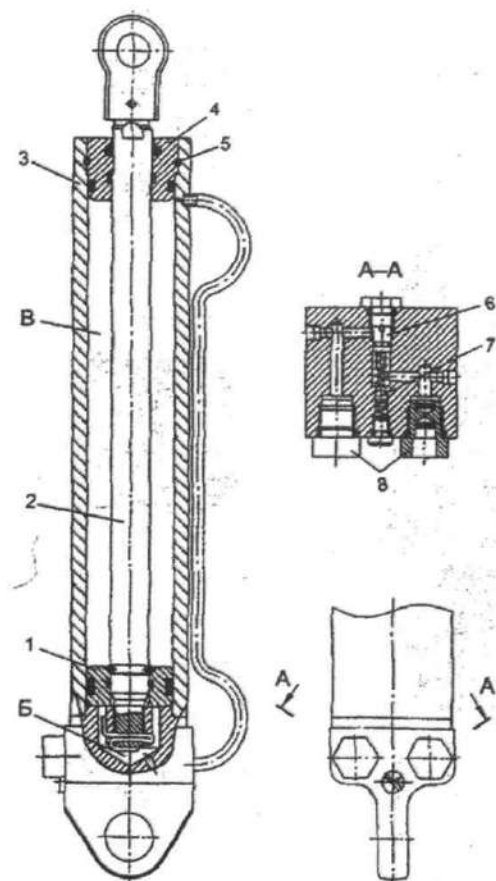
Гидроцилиндр механизма подъема кабины автомобиля:
